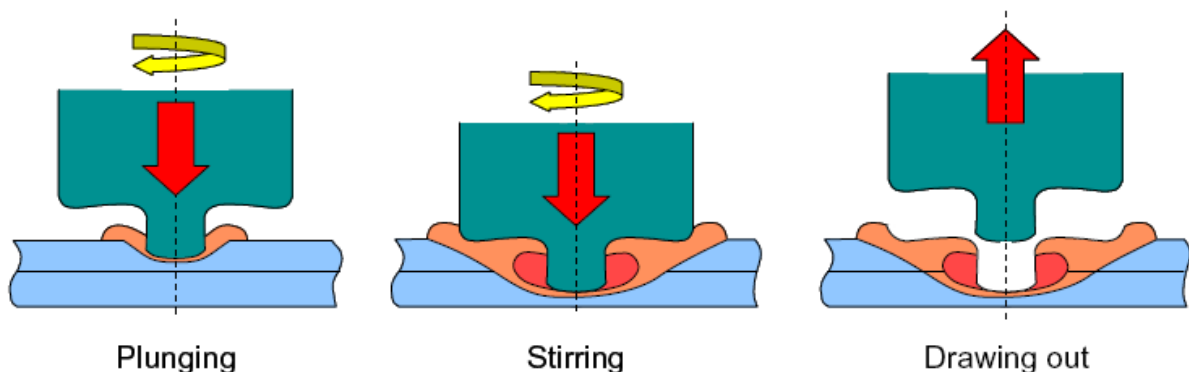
Étapes du Friction Stir Spot Welding
